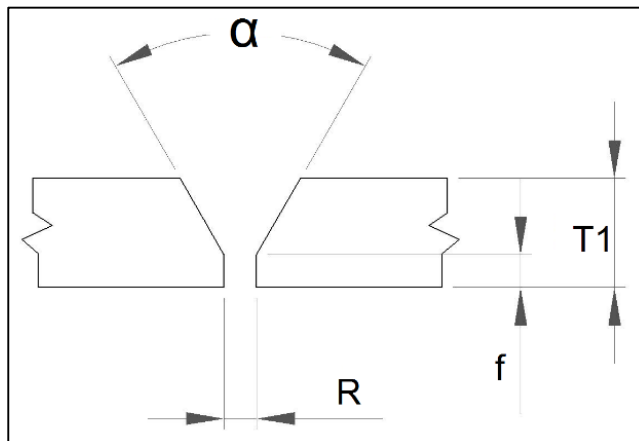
CJP - Soldadura de Canal Simple-V, Junta a Tope (B)
